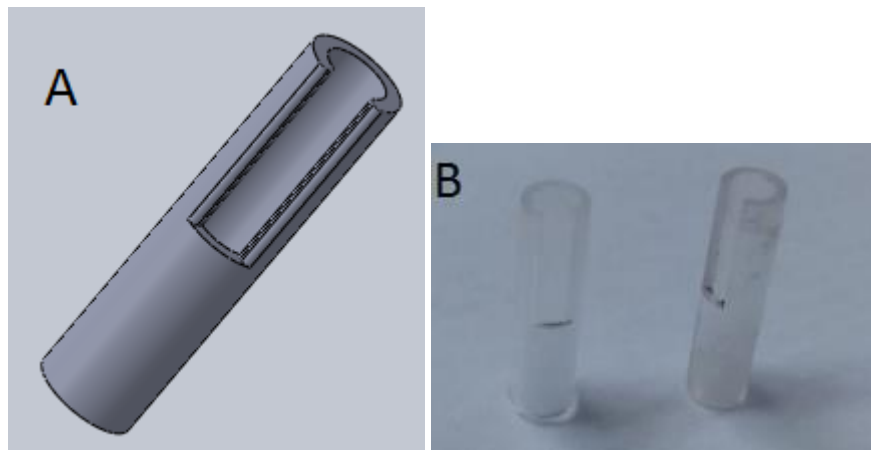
Pieza de prueba para manufactura CNC. (A) Esquema isométrico de la pieza. (B) Foto de las piezas manufacturadas.
